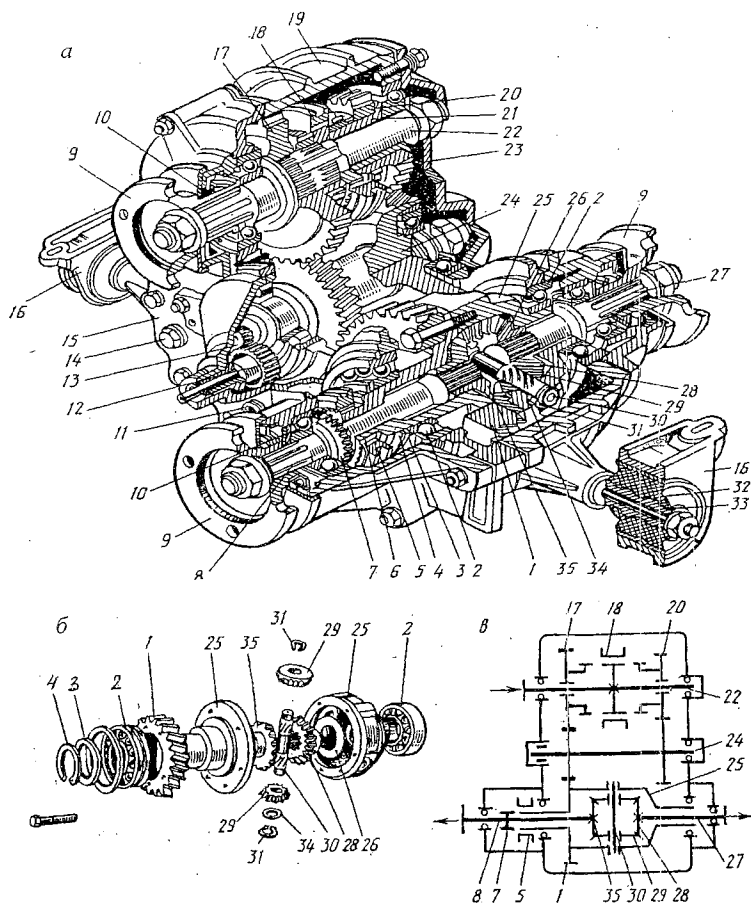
Раздаточная коробка автомобиля ВАЗ-2121 «Нива»:
